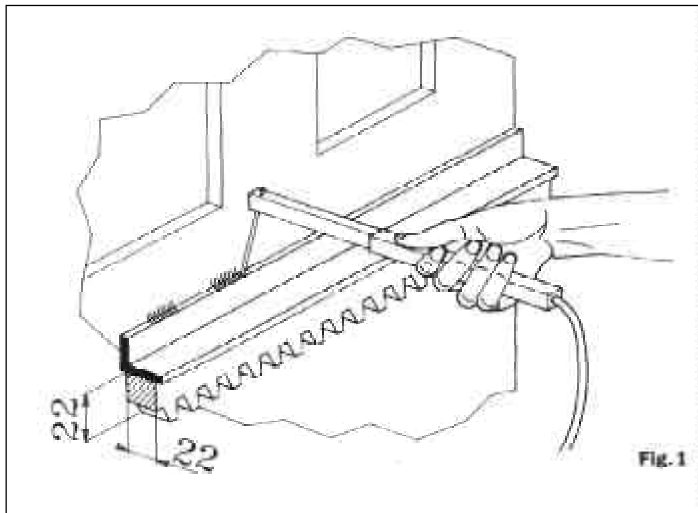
, 2 e 4 - Montaggio cremagliera - N.B.: le quote sul disegno sono in mm
